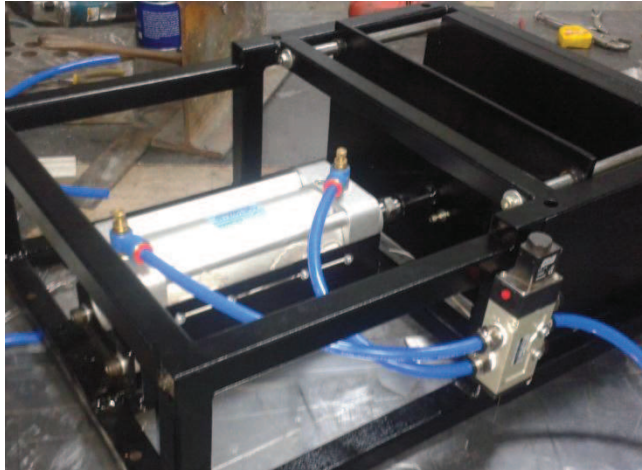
Montaje del Cilindro de Doble Efecto Seleccionado
